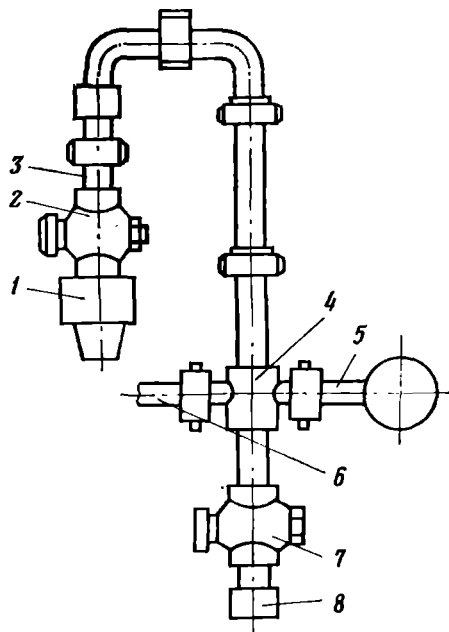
Контрольная головка-вертлюг: 1 — переводник к ведущей трубе; 2 — пробковый кран; 3 — соединительный переводник; 4 — крестовина; 5 — разделитель к манометру; 6 — отвод; 7 — пробковый кран; 8 — соединительный переводник
